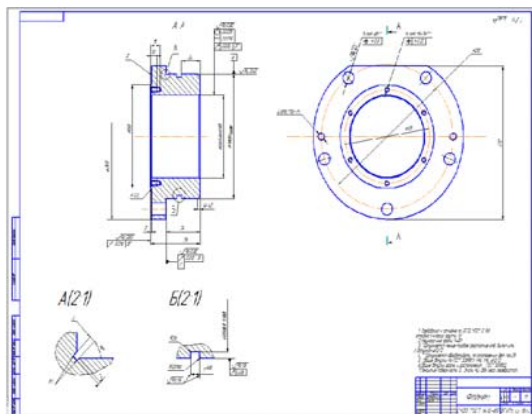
Фланец зубофрезерного станка ВСН-350
